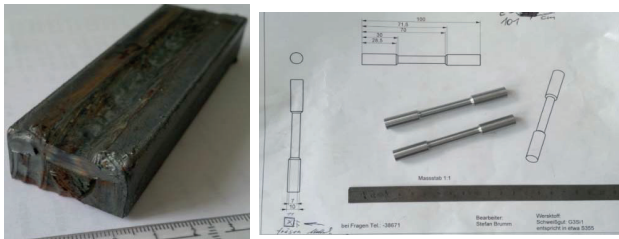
Reines Schweißgut für den Zugversuch (links) und gedrehte Zugproben (rechts)
